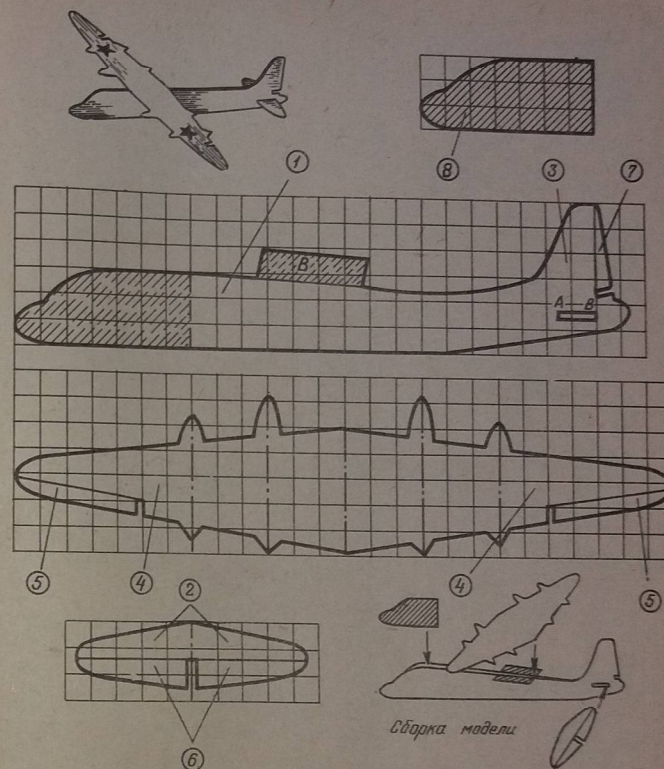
Модель самолета Ил-18: 1—фюзеляж; 2—стабилизаторы; 3—киль; 4—крылья; 5—элероны; 6—руль высоты; 7—руль поворота; 8—груз из картона
